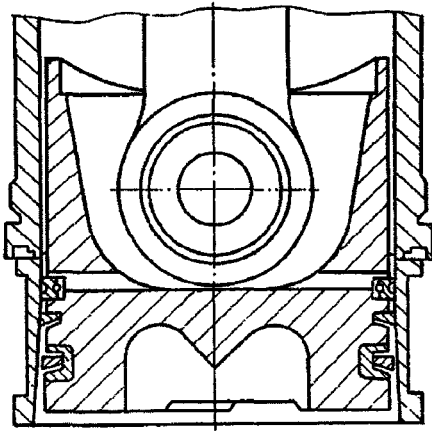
Приспособление И801.00.001-01 для установки поршня в гильзу цилиндра
